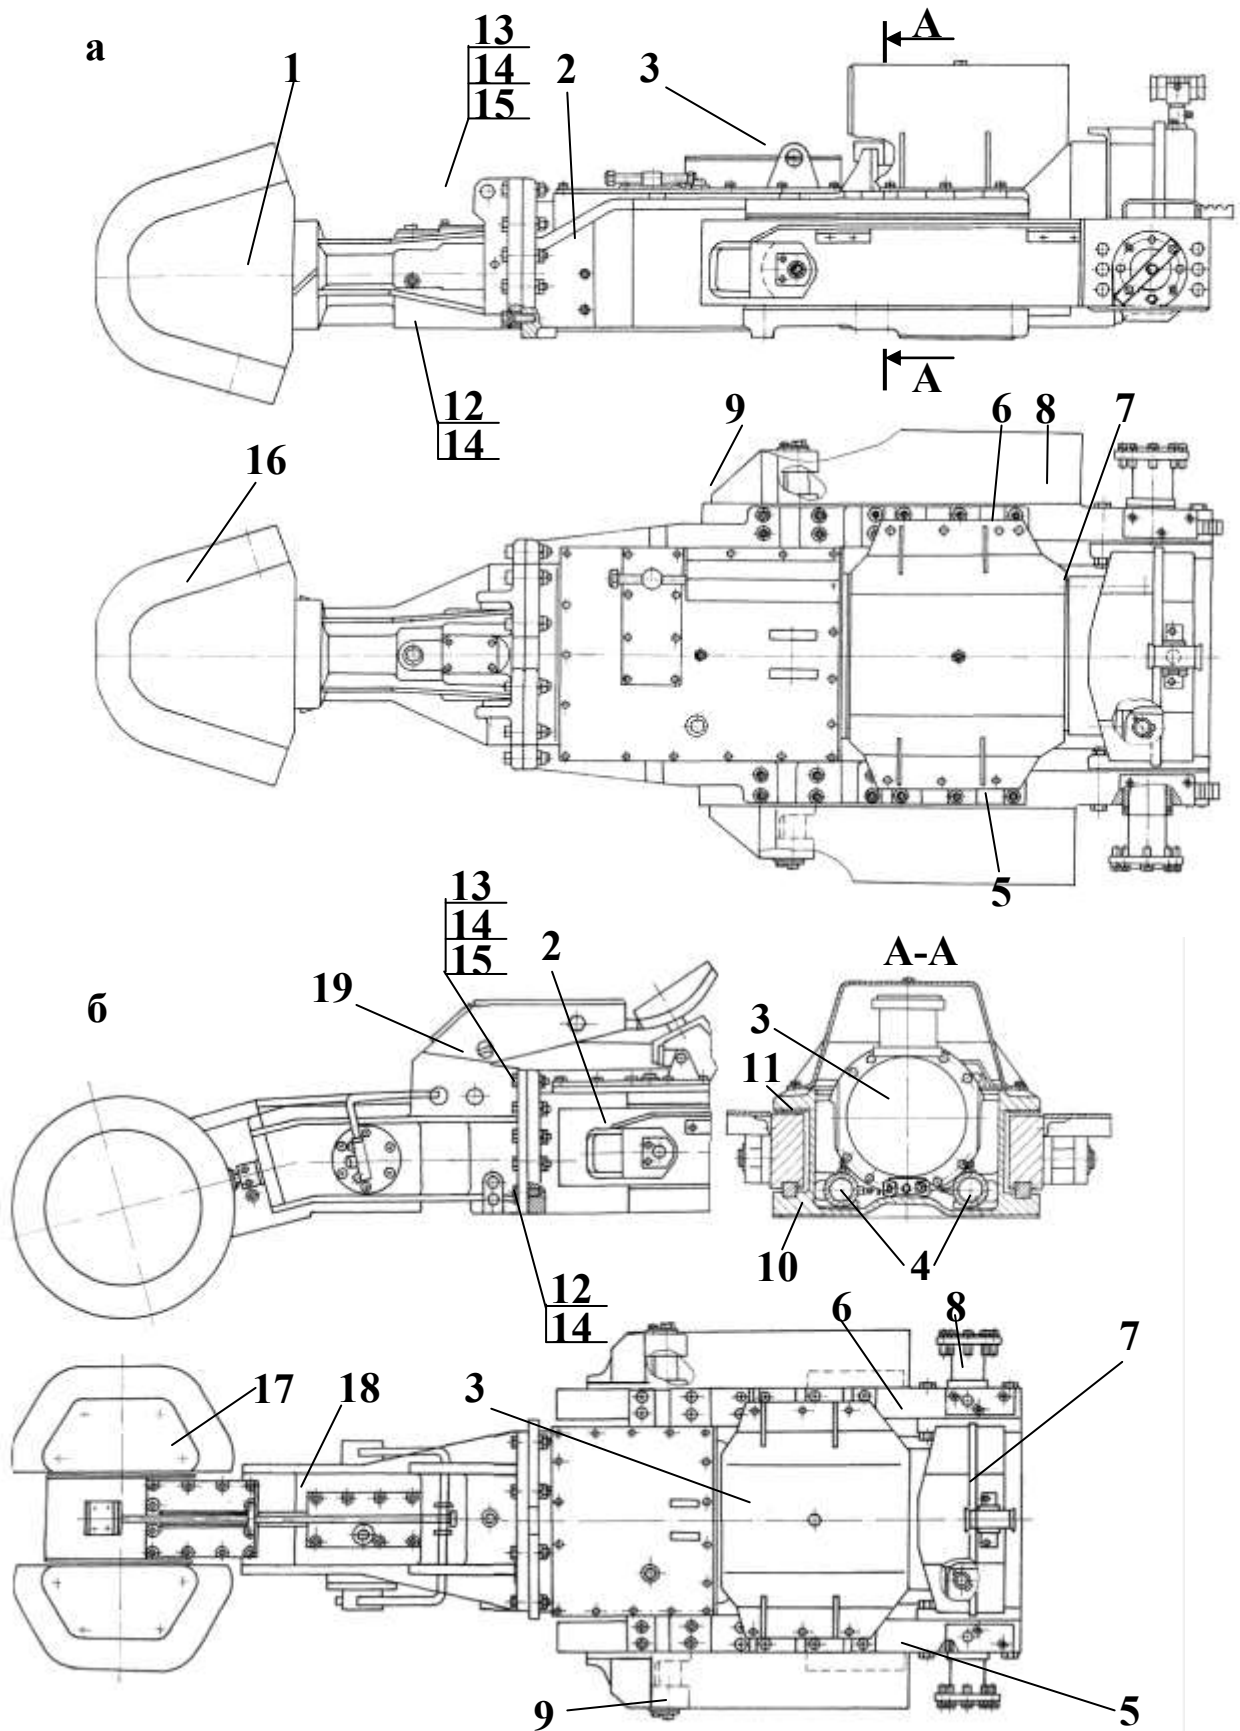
Исполнительный орган: а – с продольной конической коронкой; б – с поперечно-осевыми барабанами
